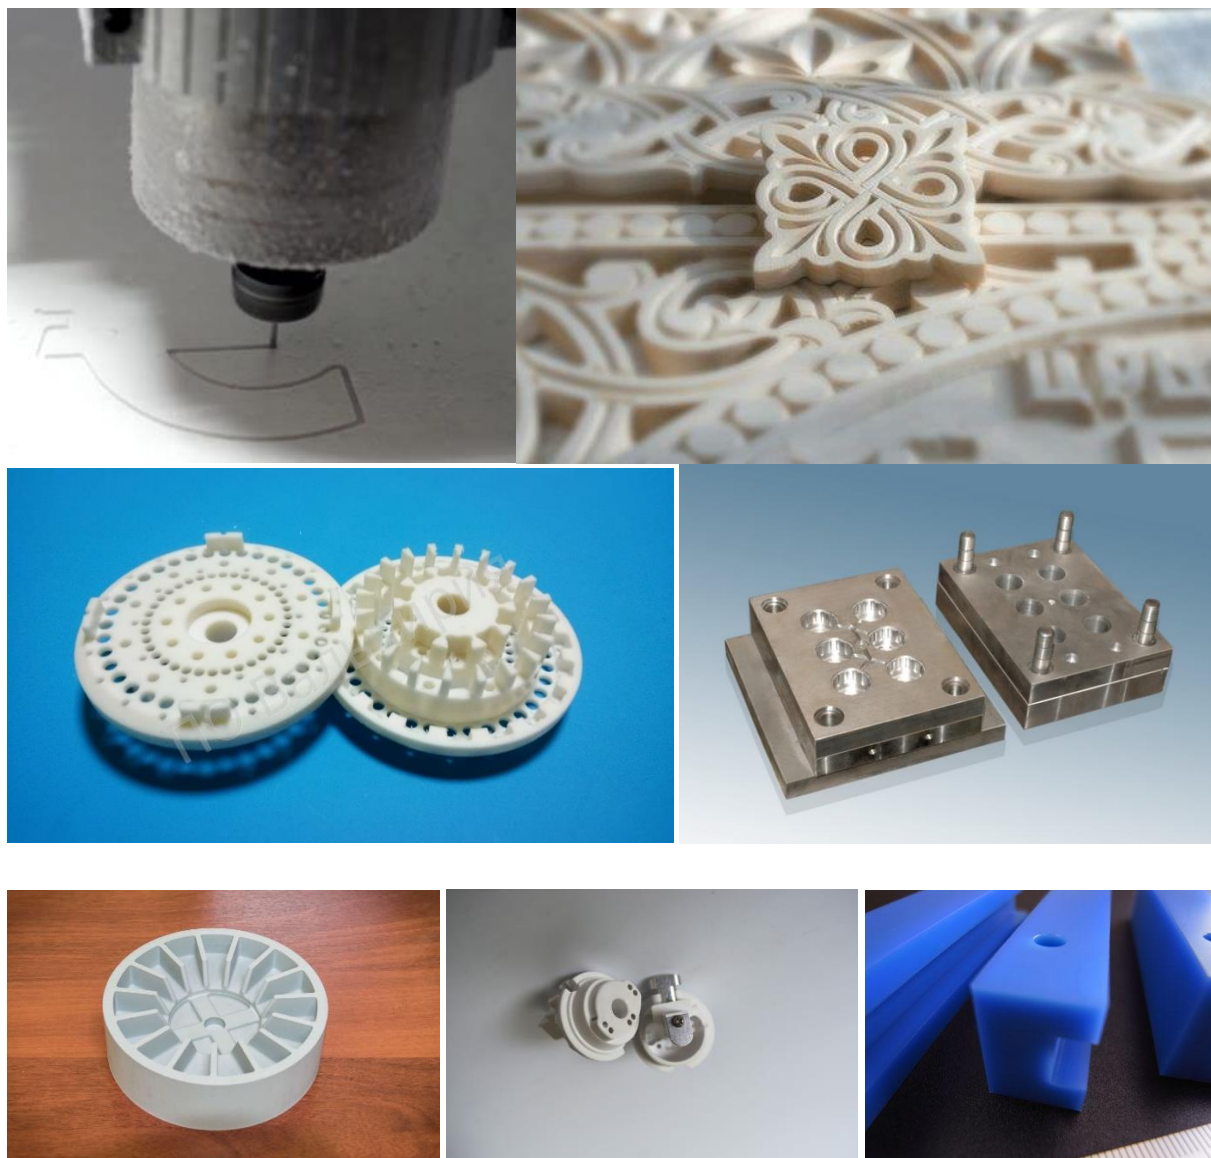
Приклади типових деталей, виготовлених на НФВ
